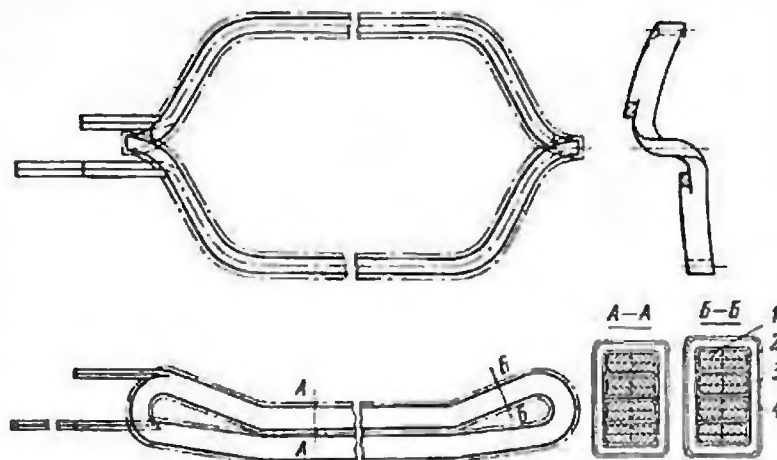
Катушка многовитковой обмотки статора асинхронного двигателя на напряжение 3000—10 000 В
